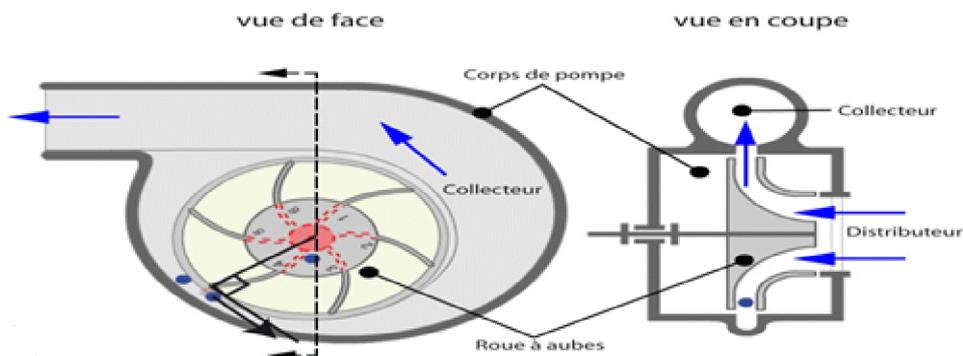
Vue de face et vue en coupe d'une pompe centrifuge.
